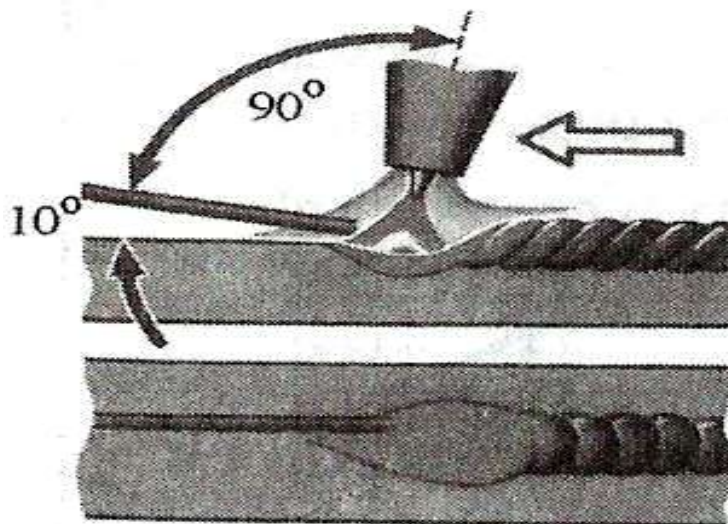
Схема введения присадочного прутка в сварочную ванну
